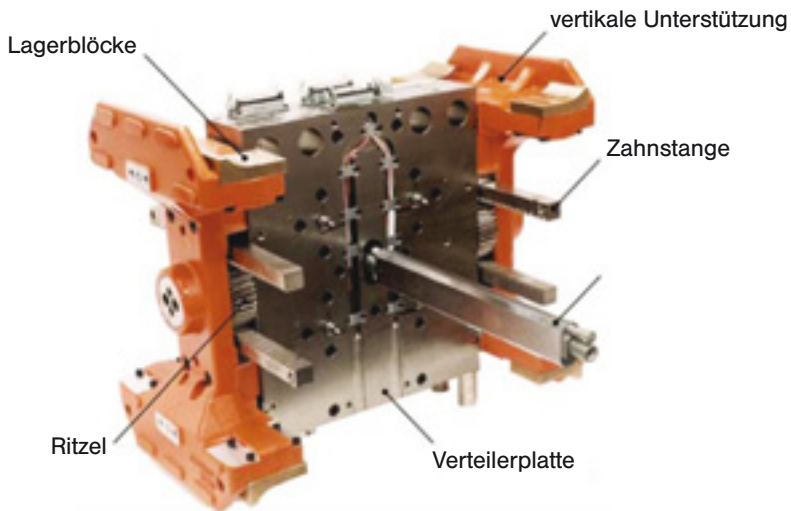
Mittelsegment eines Spritzgießwerkzeugs mit Zahnstangenauswerfergetriebe [13.12]
